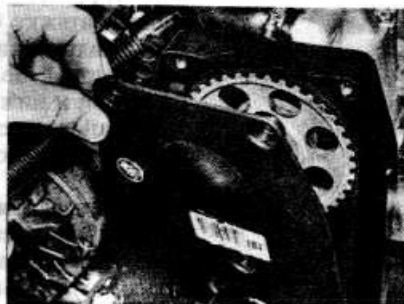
и отсоедините верхнюю крышку ремня — двигатель 1,6 л с многоточечным впрыском топлива
